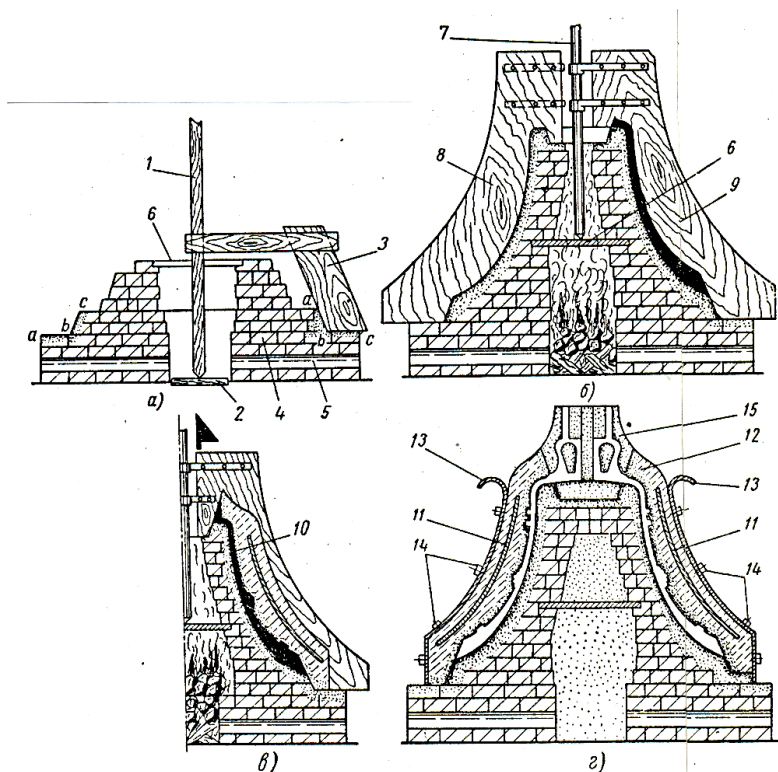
Схема изготовления литейной формы колокола: а - выкладка цоколя (1 - стойка, 2 - гнездо, 3 - шаблон, 4 - цоколь с замком абс, 5 - каналы для выхода газов, 6 - железный крест); б - формовка по шаблону стержня колокола и тела колокола (7 - шпindelь, 8 - шаблон для внутренней стенки колокола, 9 - шаблон для внешней стенки колокола); в - изготовление глиняной формы колокола (10 - тело-рубашка колокола); г - разрез собранной формы колокола (11 - железные полосы-ребра, 12 - внешняя поверхность, 13 - внешние железные ребра, 14 - стягиваемые болты, 15 - коническое гнездо коронки колокола)
